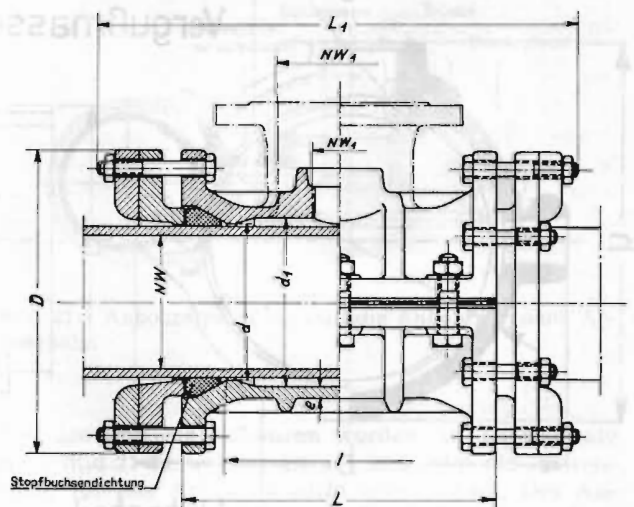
Geteilter Anbohrüberschieber für obere oder seitliche Anbohrung mit Gewinde- oder Flanschabgang
